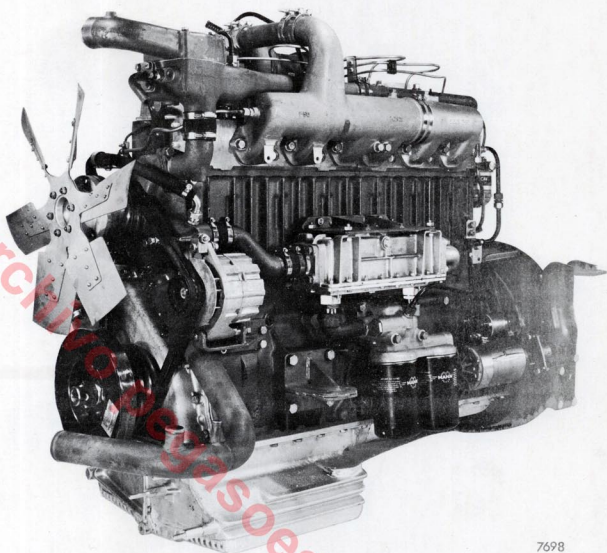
Motor 9222 y derivados (lado izquierdo)
